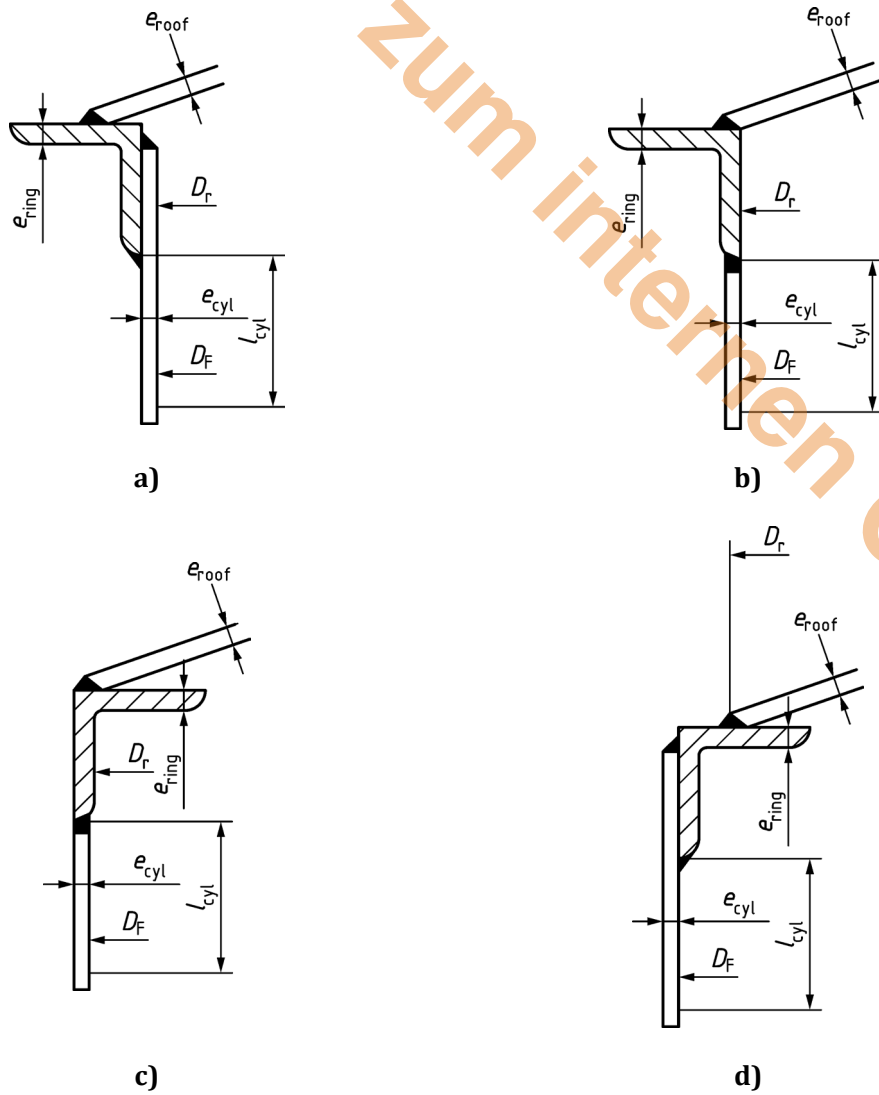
Verbindungen zwischen Dach und oberem Mantelschuss: Dach am Dacheckring angeschweißt
